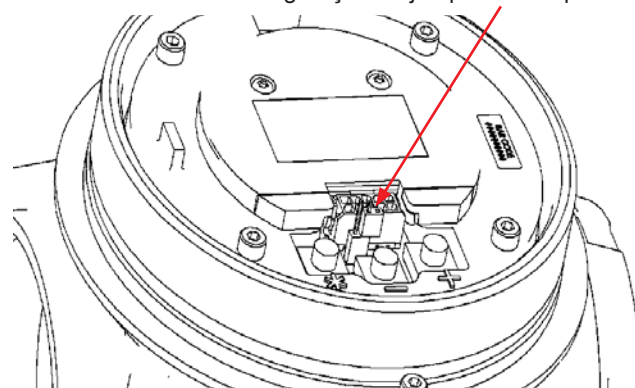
Visualização frontal do cabeçote do instrumento, com a tampa principal removida
